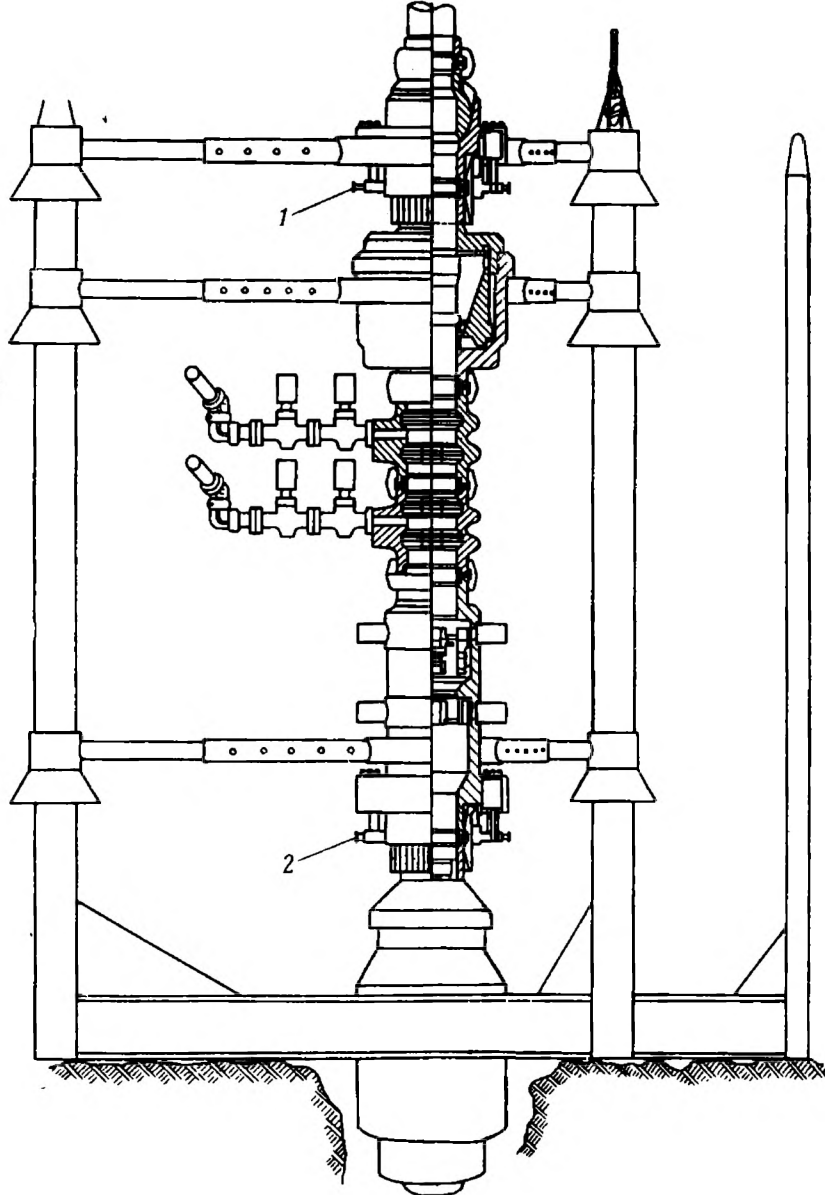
Превенторный узел, соединенный с устьевым оборудованием при помощи соединительных приспособлений «коллет коннектор» с гидроравлением.
